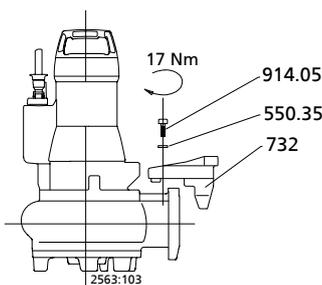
Halterung montieren bei Seilführung, 1-Stangenführung und Bügelführung
